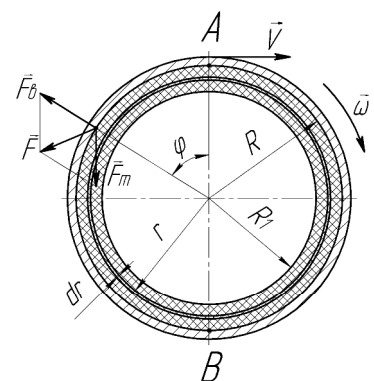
Поперечний переріз циліндричної форми з композицією та схема діючих сил під час відцентрового формування
